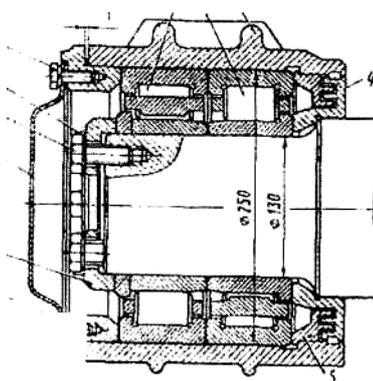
Букса грузового вагона с двумя цилиндрическими подшипниками с торцевым креплением тарельчатой шайбой и четырьмя болтами
